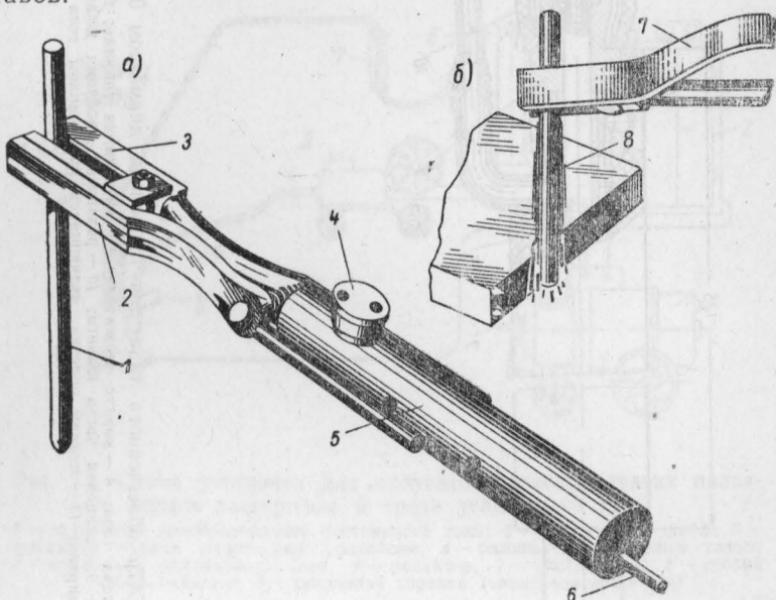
Резак РВД-1-57 для воздушно-дуговой резки
